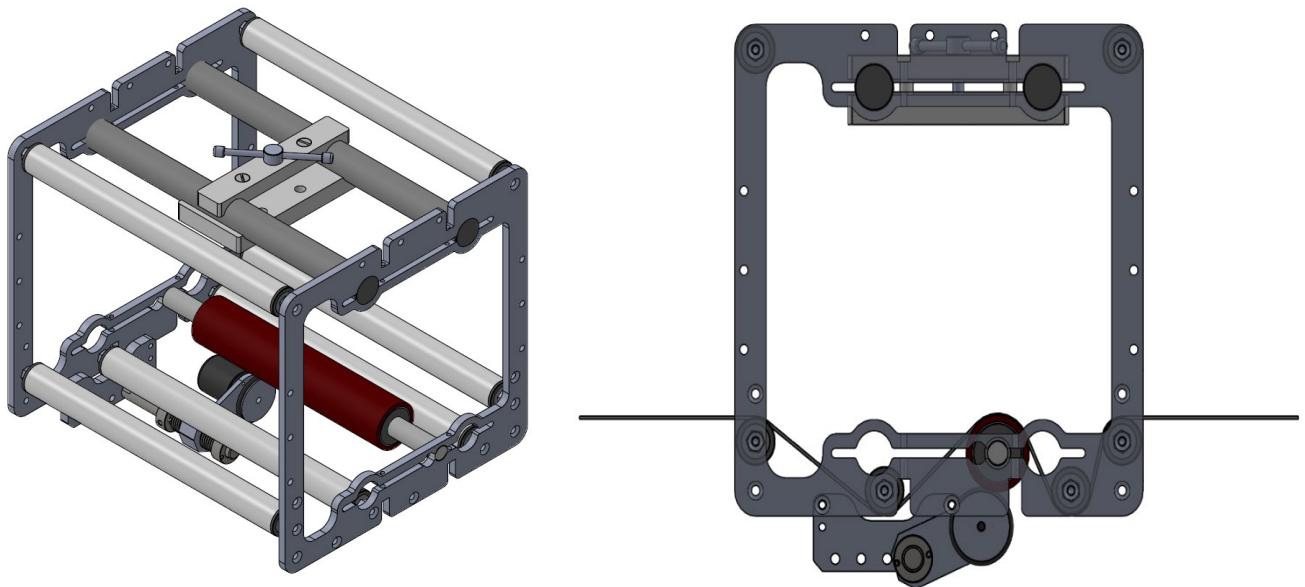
Система протяжки запечатываемого упаковочного материала?
